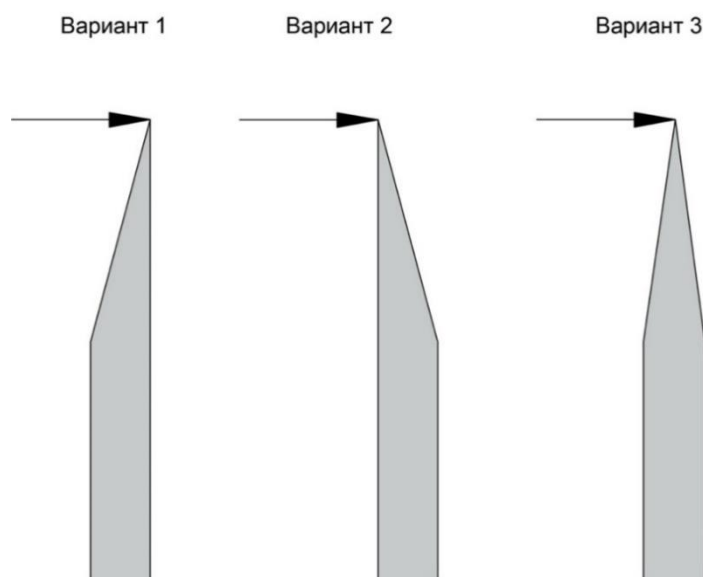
Варианты заточки скребка исполнительного органа устройства улавливания ленты конвейера (стрелкой показано направление движения оборвавшейся конвейерной ленты)
